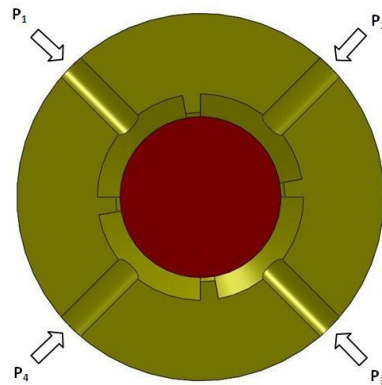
Schéma de principe d'un palier hydrostatique : coupe transversale
